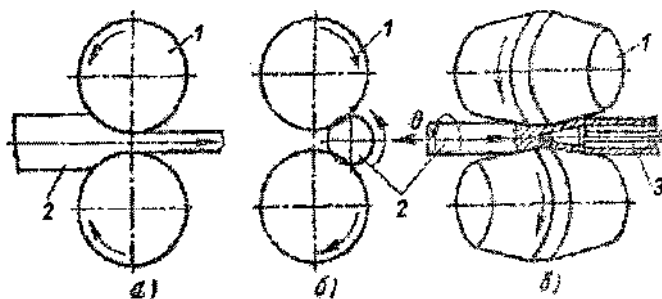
Схемы прокатки: 1 - валки; 2 - заготовка; 3 - оправка
